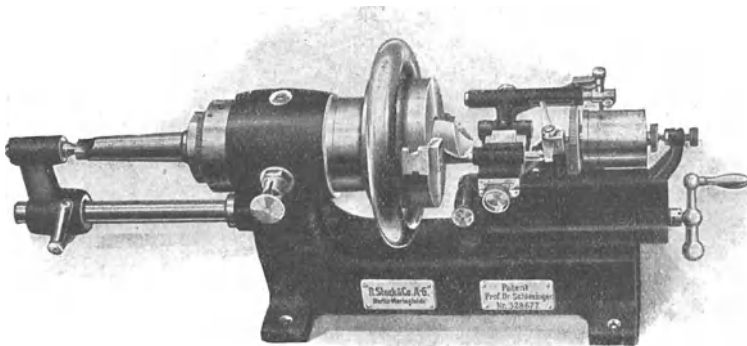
Freiwinkel-Meßmaschine. (R. Stock & Co., Berlin.)
